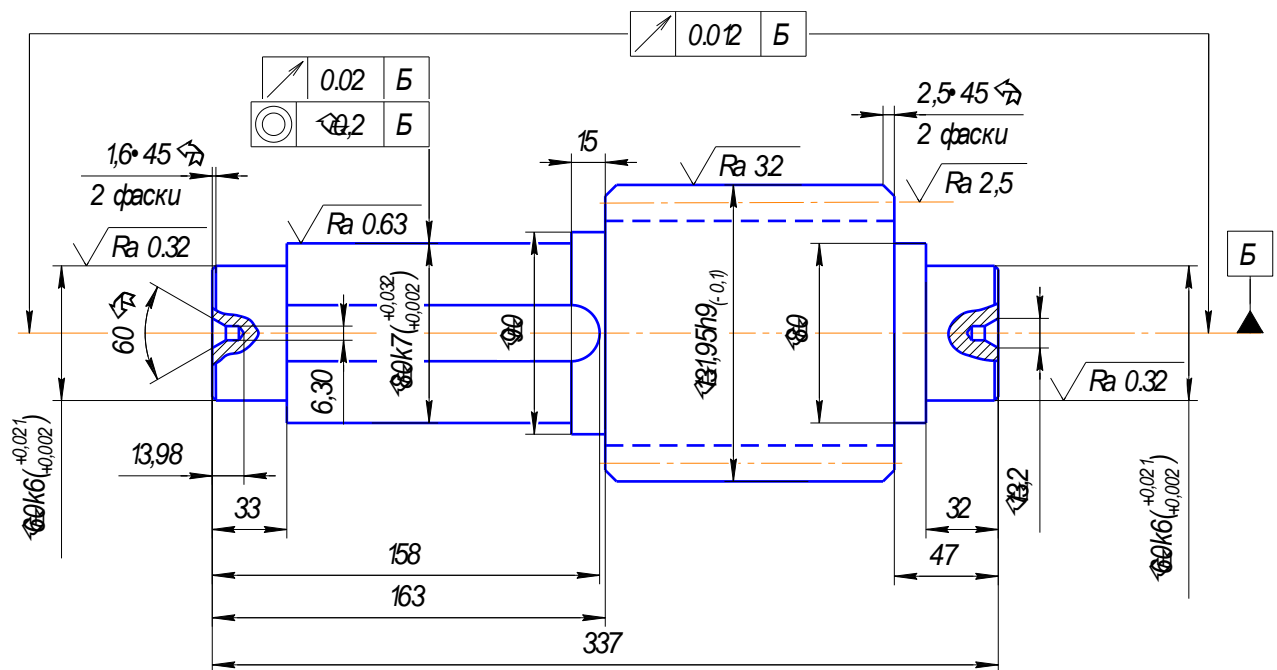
Робоче креслення вал-шестерні редуктора
